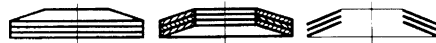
Tellerfederpaket (Teller gleichsinnig geschichtet)
